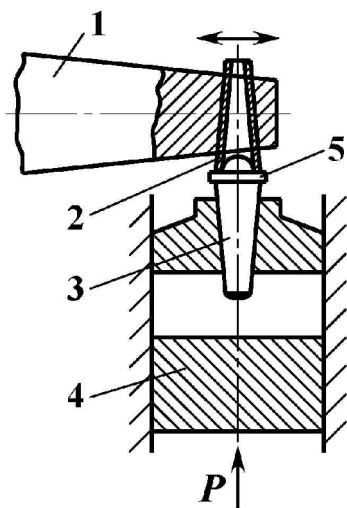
Ультразвуковая сварка по контуру: 1 – волновод; 2 – сменный полый штифт; 3 – сменный прижимной штифт; 4 – прижимная опора; 5 – свариваемое изделие
